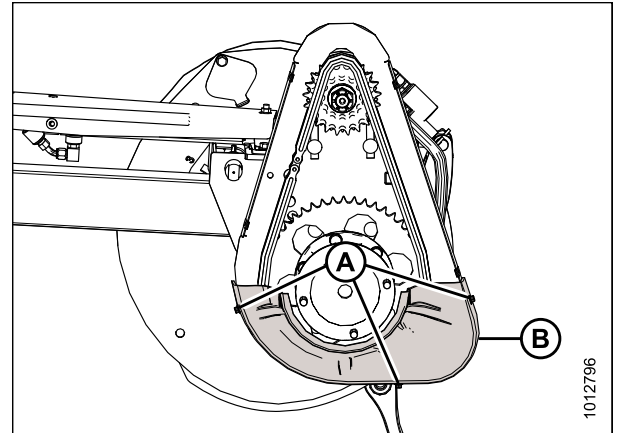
Tampa inferior da transmissão (tampa superior removida)
